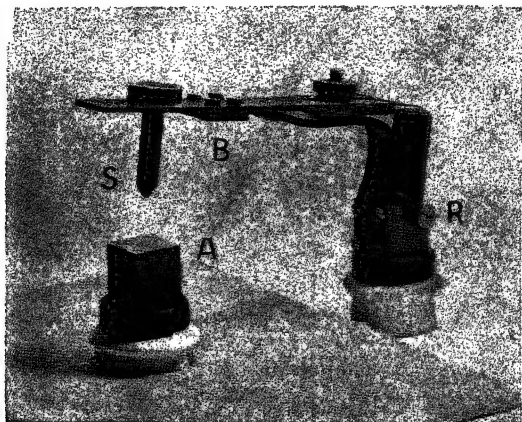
Die Elektroden einer Punktschweißanlage
